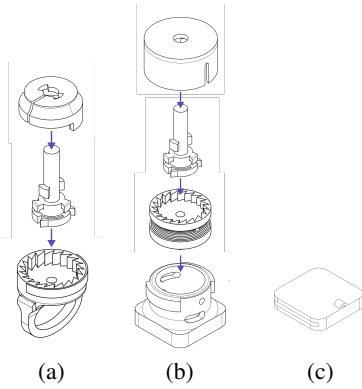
Dibujos CAD de los componentes del dispositivo de tensionado (DdT). Anillo (a), bobina (b) y auxiliar (c).
